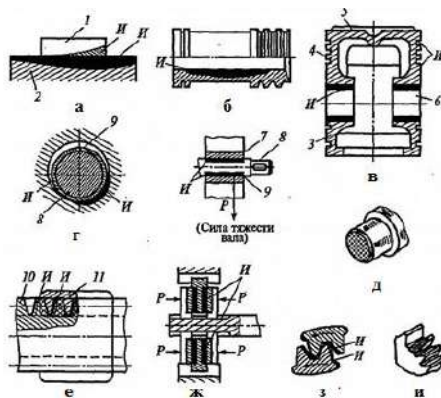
Характер механического износа деталей: а - направляющих станины и стола; б - внутренних поверхностей цилиндра; в - поршня; г, д - вала; е - резьбы винта и гайки; ж - дисковой фрикционной муфты; з, и - зубьев колеса; 1 - стол; 2 - станина; 3 - юбка; 4 - перемычка; 5 - днище; 6 - отверстие; 7 - подшипник; 8 - шейка вала; 9 - зазор; 10 - винт; 11 - гайка; И - места износа; Р - действующие усилия
